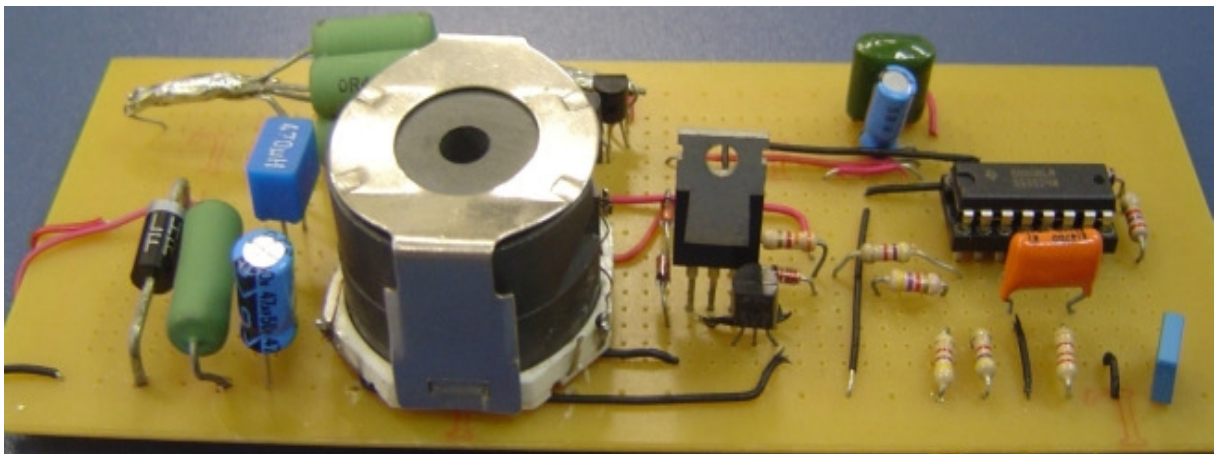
Protótipo do Conversor DC-DC montado em placa padrão - 2
